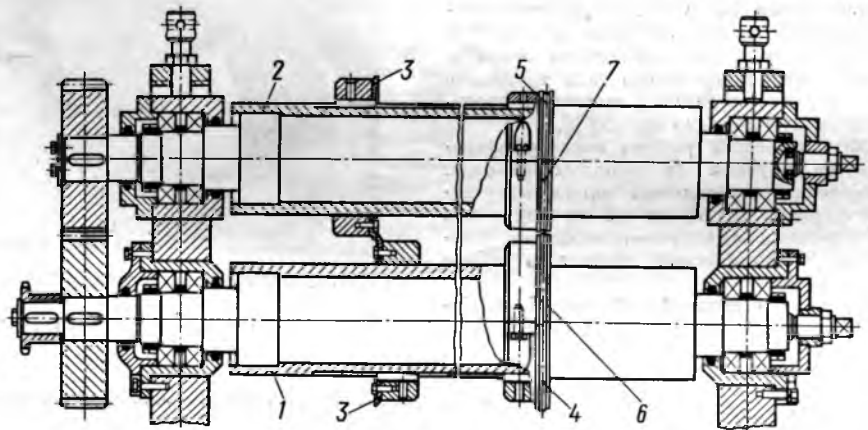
Схема станка для резки и рилевания гофрированного картона
